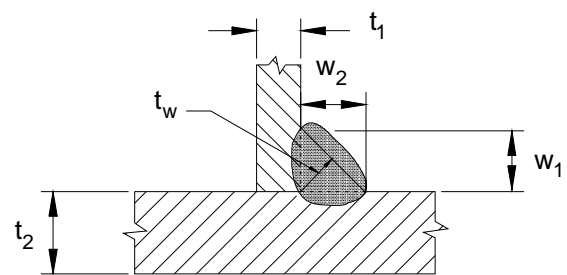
B Soldaduras de filete - Unión en T
